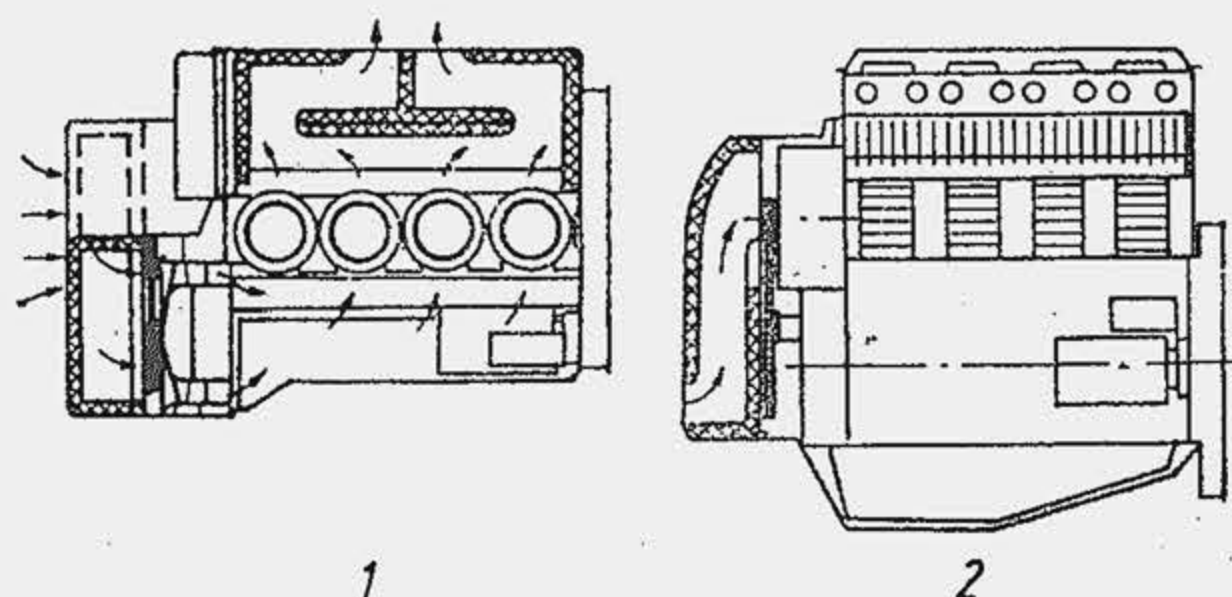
Izolarea fonică integrală a unui motor răcit cu aer:
